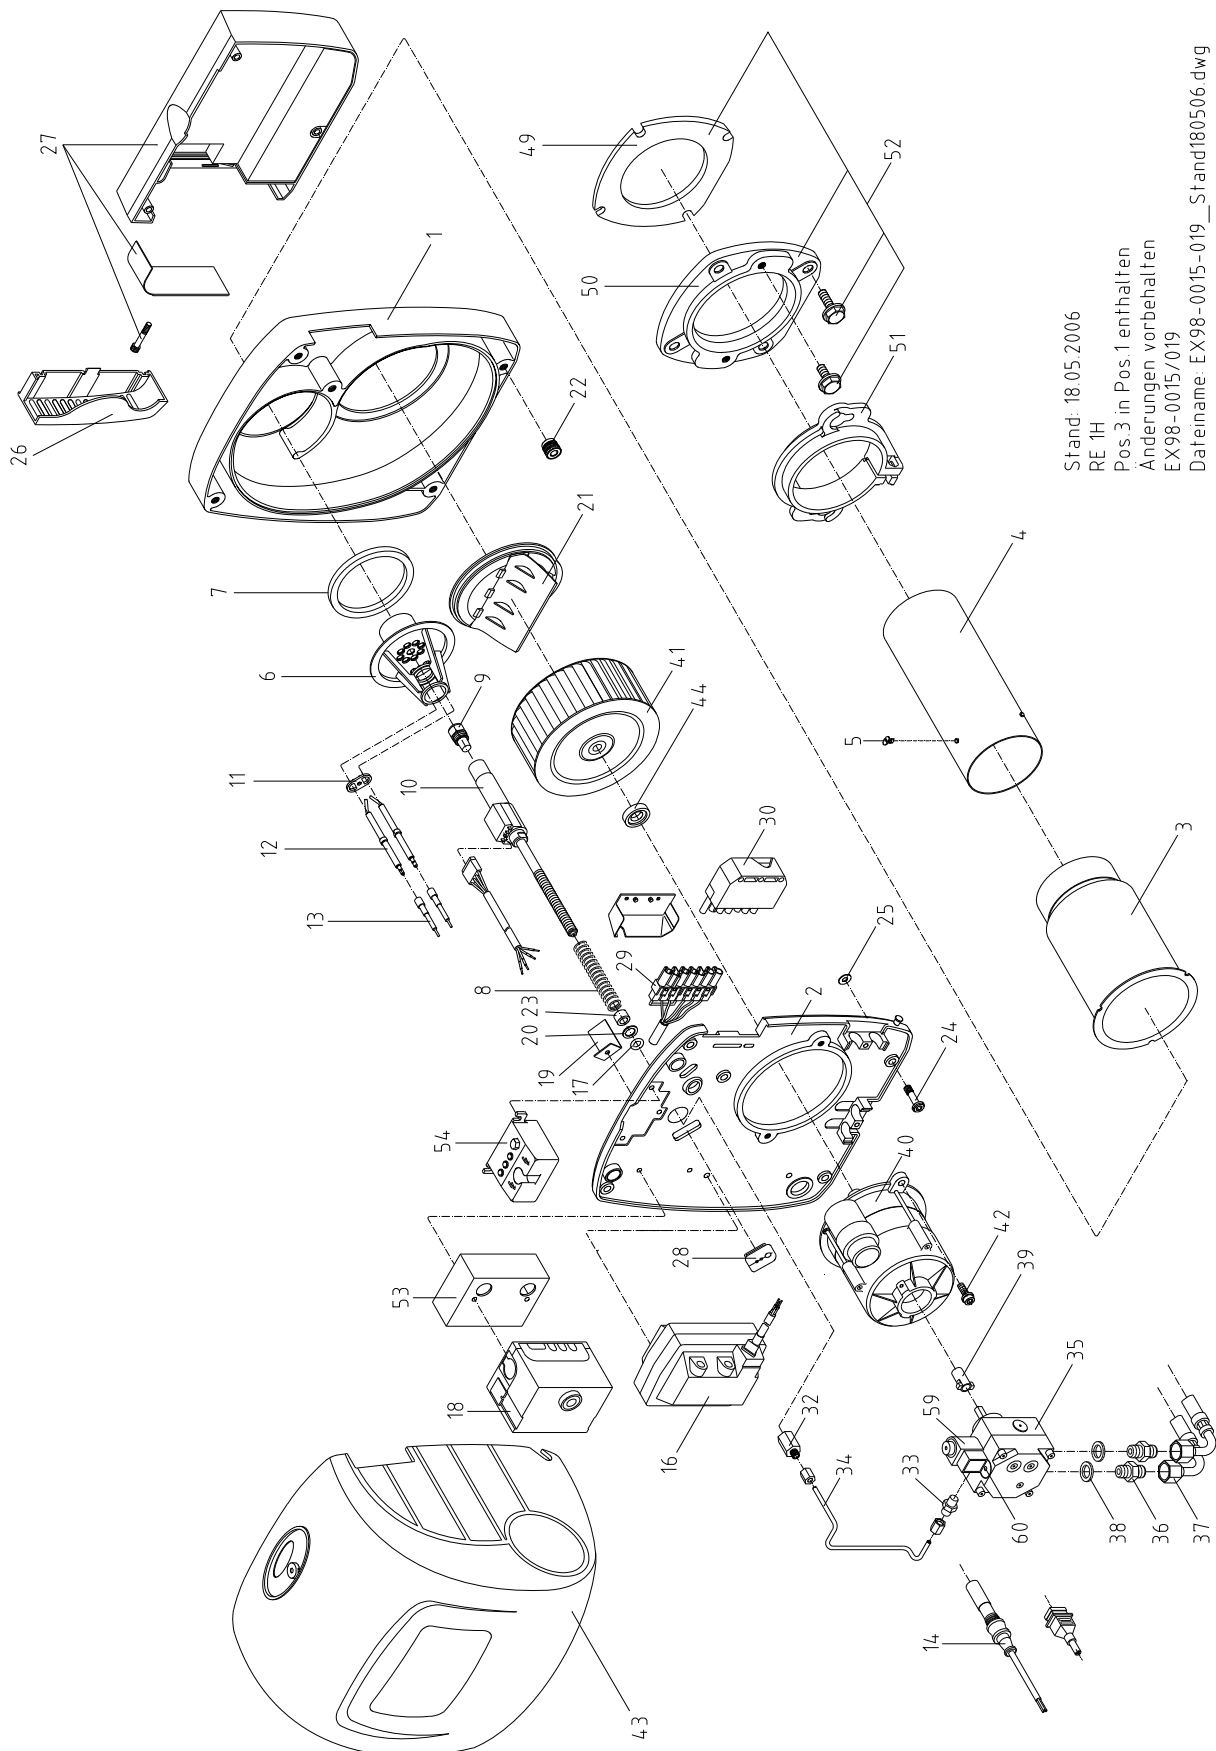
Explosionszeichnung RE 1H / RE 1 HK
